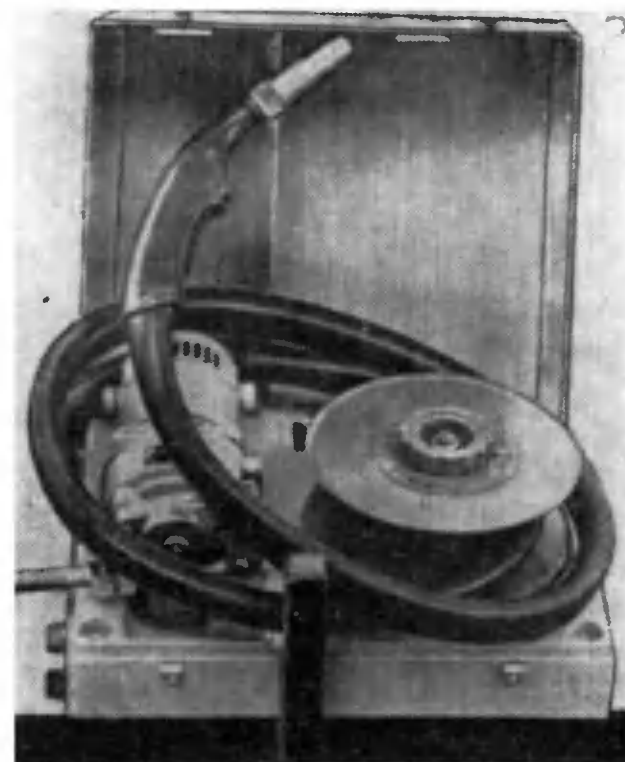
Сварочный полуавтомат ПДГ-305.
